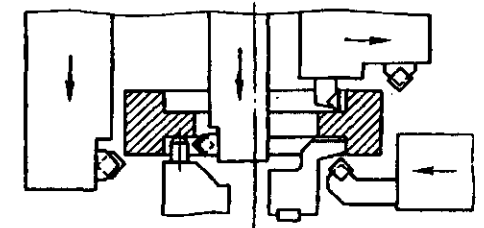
Наладка двухшпиндельного вертикального токарного полуавтомата для обработки заготовки зубчатого колеса
